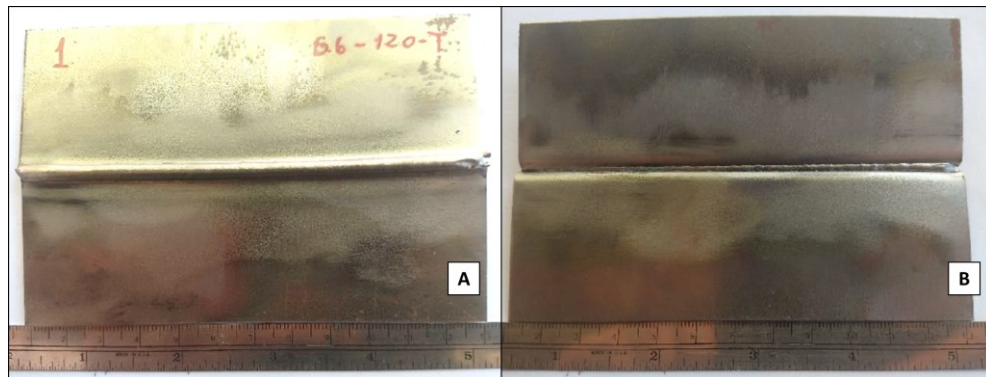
Condição 1 de soldagem GMAW. A) vista de cima da chapa soldada B) Vista do verso da solda (Próprio autor)
